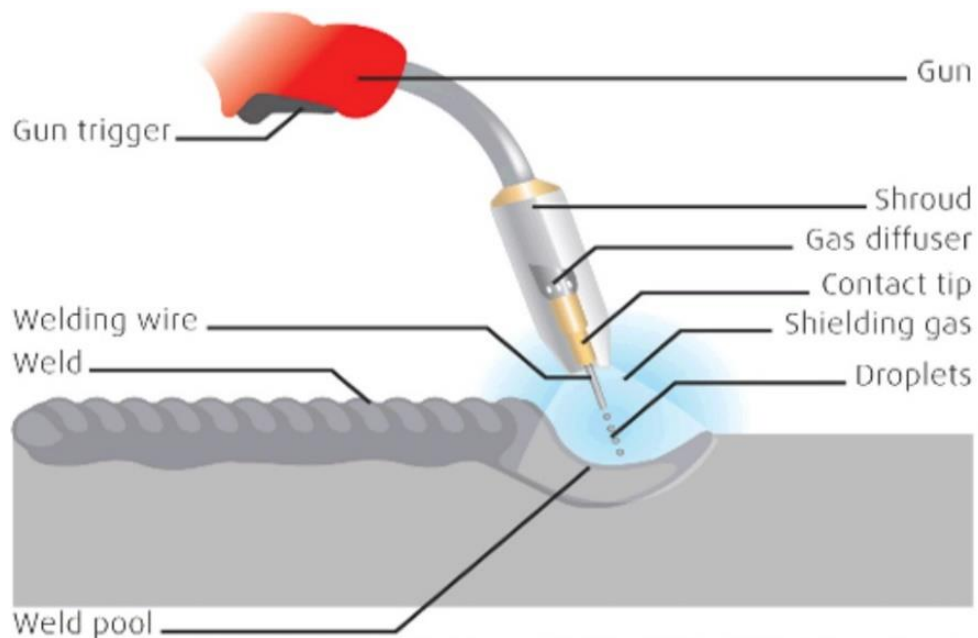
Componentes da tocha de soldadura (What Is Mig Welding /Gas Metal Arc Welding | Sparker Electric Ltd., 2018)
